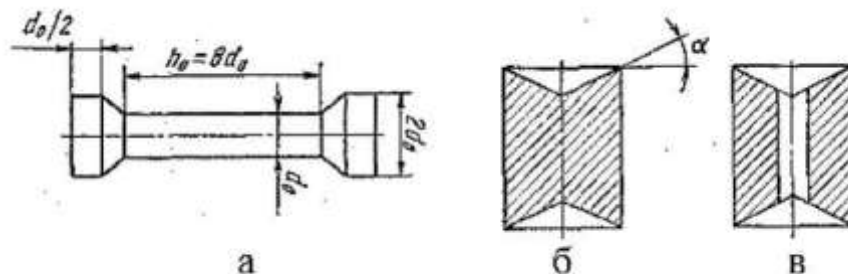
Можливі форми зразків для випробування на стиск: а) циліндричний подовжений зразок з головками для прецизійних вимірювань, б) стандартний зразок, в) зразок з видаленою серцевиною для випробувань крихких матеріалів
